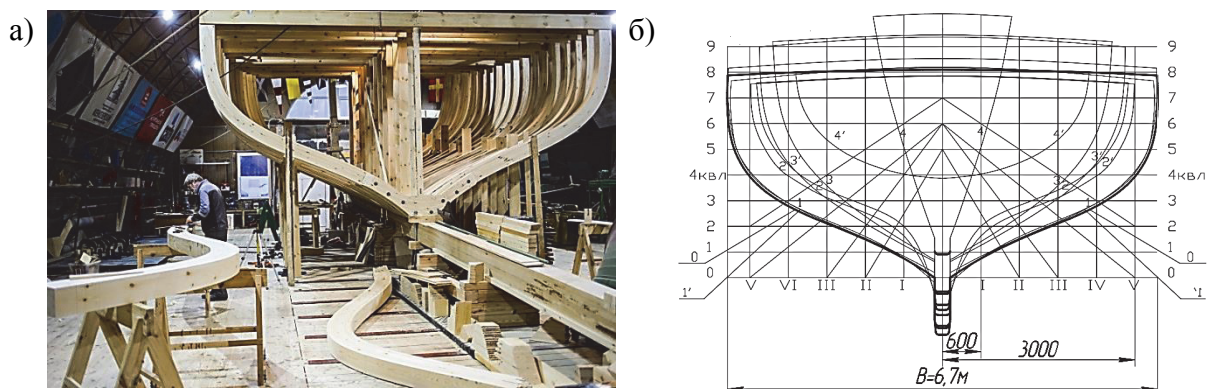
Поморское судно: корпус в постройке (а); Чебышевский корпус (б)
